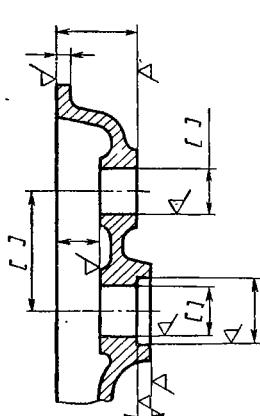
Нанесение размеров на чертеже детали, обрабатываемой совместно с другой деталью (до сборки)
